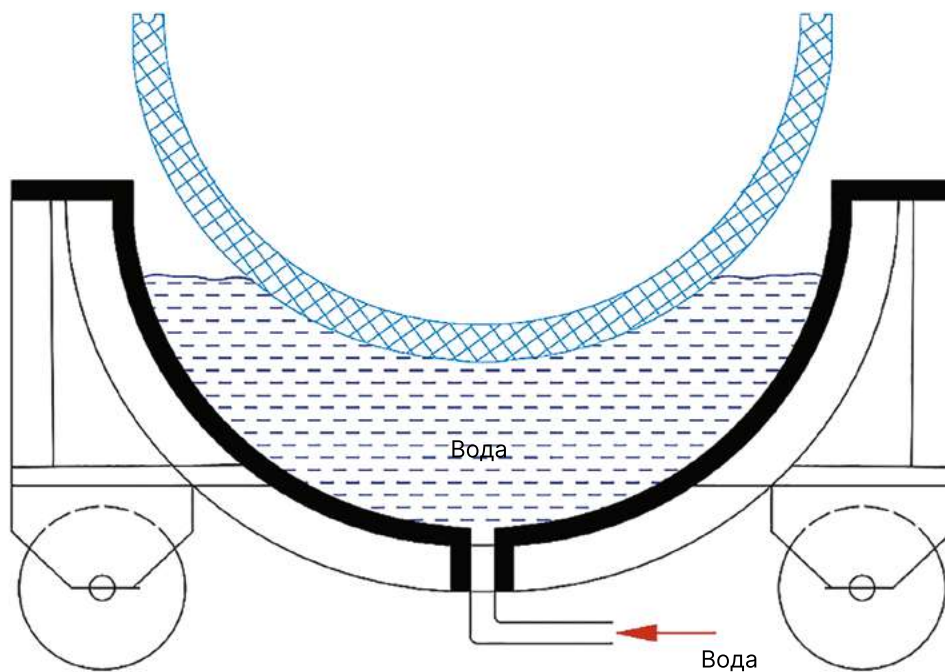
Разделение акриловой заготовки от вогнутой пресс-формы (матрицы) под напором воды
